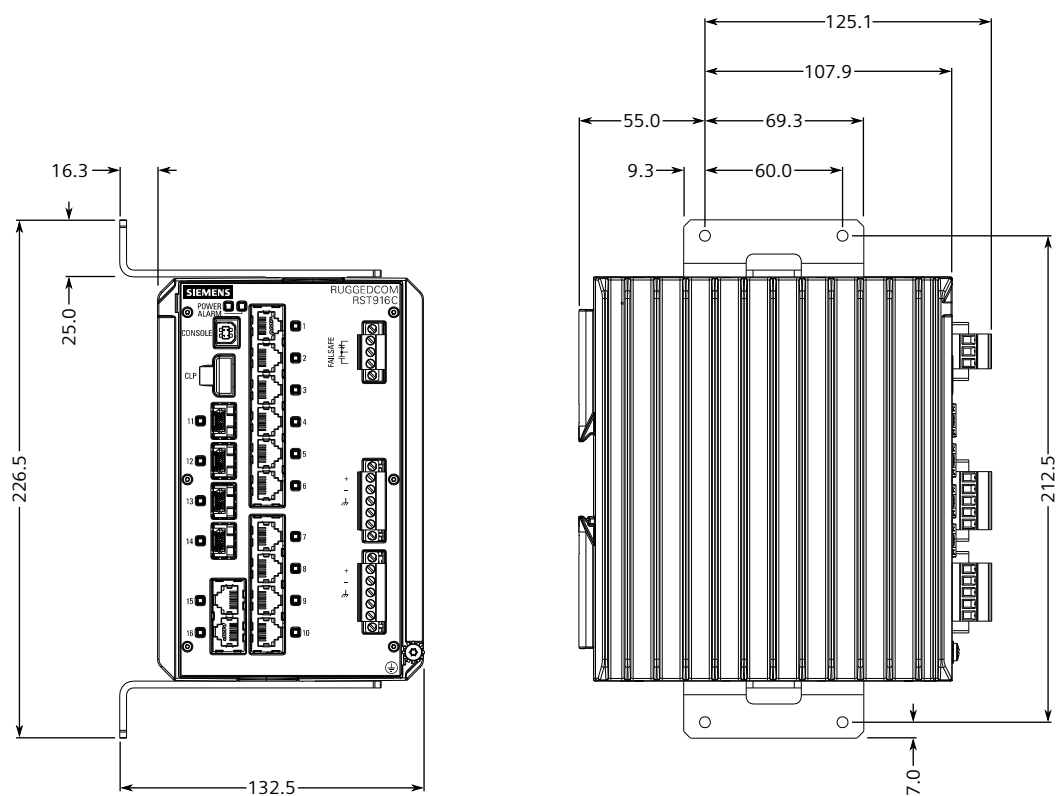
Размеры при монтаже на панель (монтаж на боковой стороне)
